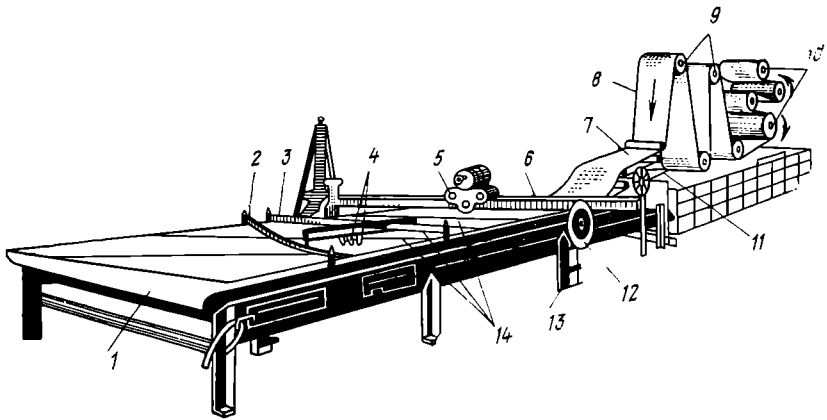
Горизонтальная диагонально-резательная машина для раскроя обрезиненного корда: 1 — стол с ленточным транспортером; 2 — направляющая; 3 — мерительный механизм; 4 — фотоэлементы; 5 — режущий механизм; 6 — поперечная балка; 7, 11 — приемные транспортеры; 8 — обрезиненный корд; 9 — компенсатор; 10 — каретка с обрезиненным кордом; 12 — штурвал; 13 — педаль; 14 — отрезанные полосы корда.
